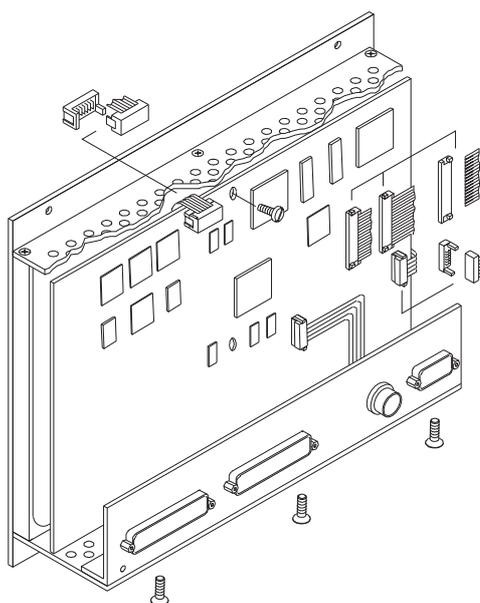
Befestigen der Einheit aus Anschlussplatte und Hauptplatine
